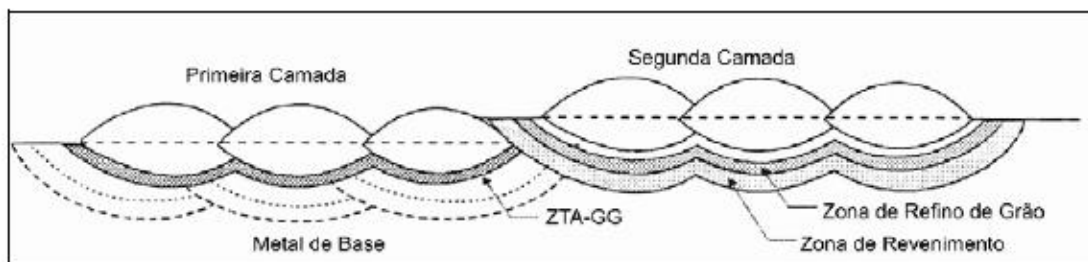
Esquema das sub-regiões da ZTA em uma soldagem multipasses.
